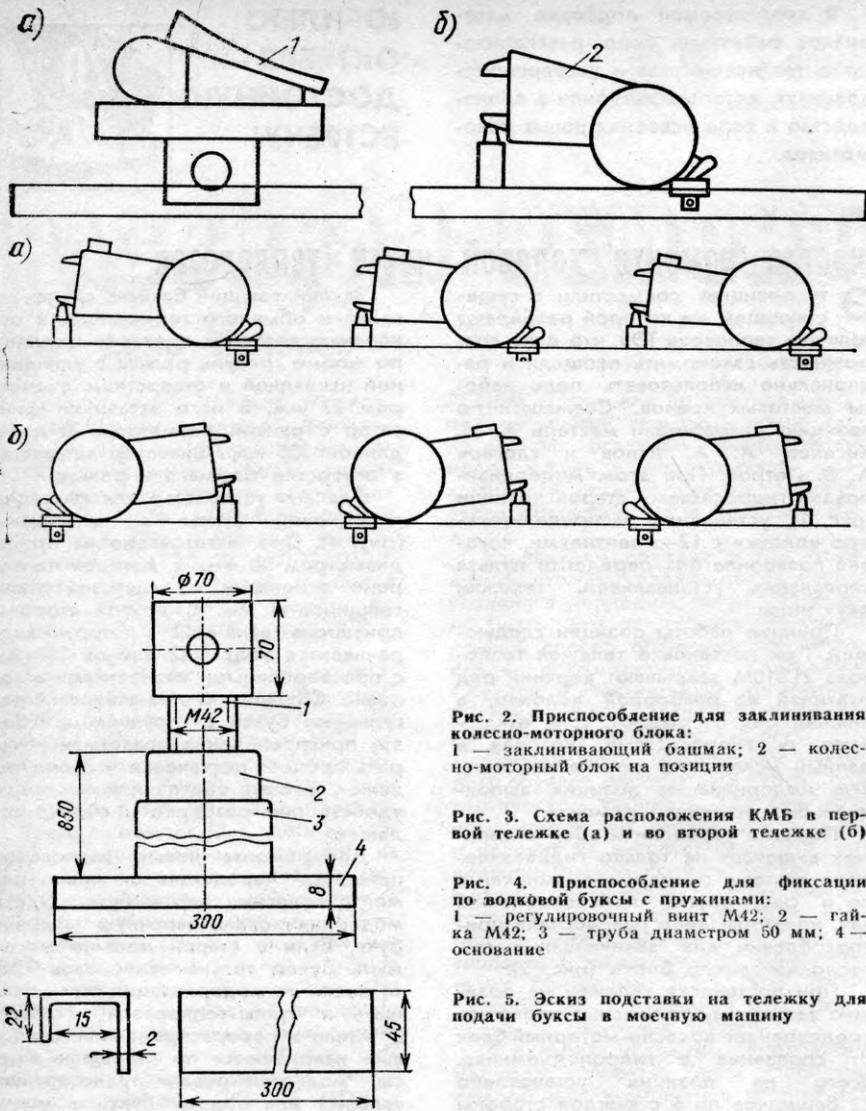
Приспособление для заклинивания колесно-моторного блока:
